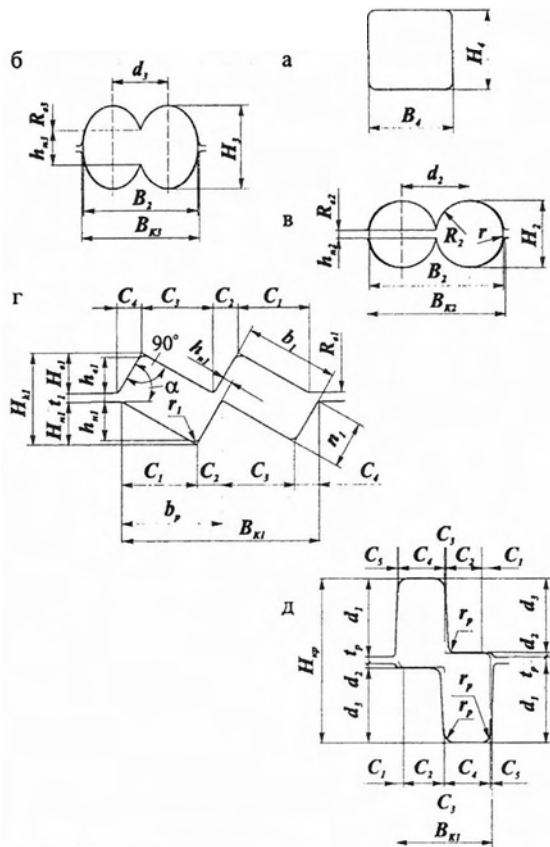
Схема калибровки валков для двухручьевой прокатки-разделения сортовых профилей с продольным разделением раската срезом перемычки; а + д - очередность расположения калибров.
